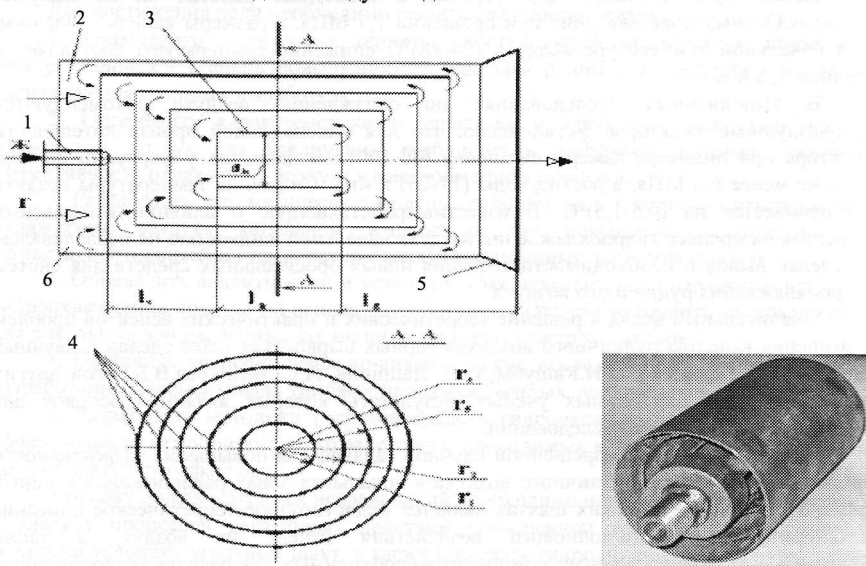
Схема и фотография многокамерного водоежектора: 1 - сопло; 2 - камера; 3 - камера смешивания; 4 - цилиндры; 5 - диффузор; 6 - конфузор.
